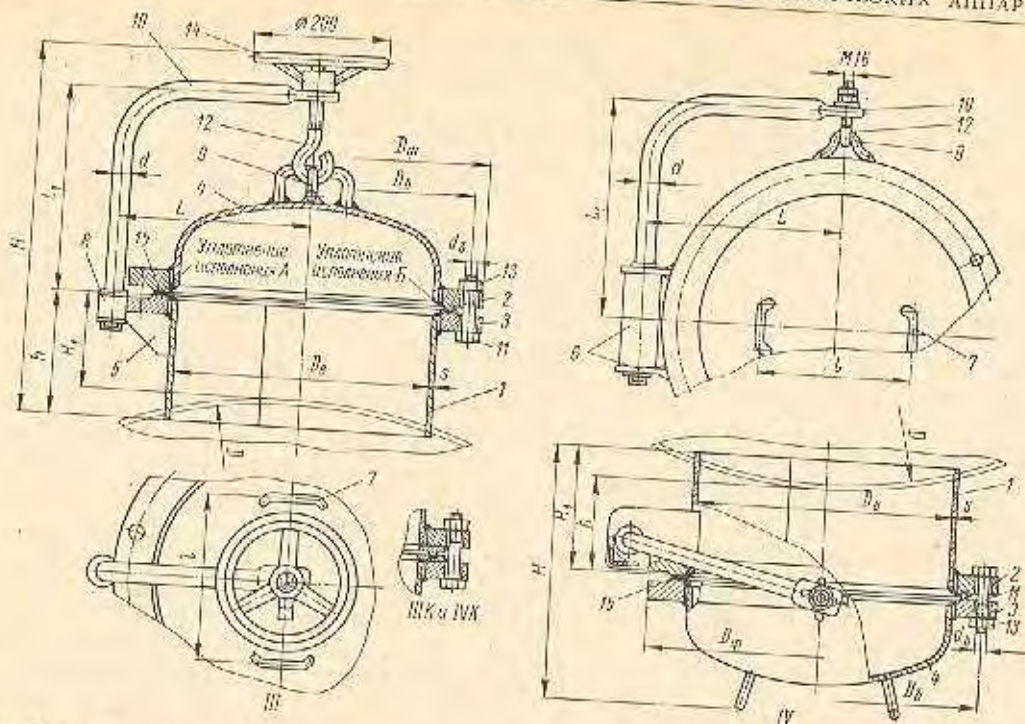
Конструкция люков с эллиптической фланцевой крышкой и подъемно-поворотным устройством для стальных аппаратов на $p_d \leq 2,5 \text{ МПа}$ (табы III, IIIK; IV и IVK по ОН 26-01-10-65)
